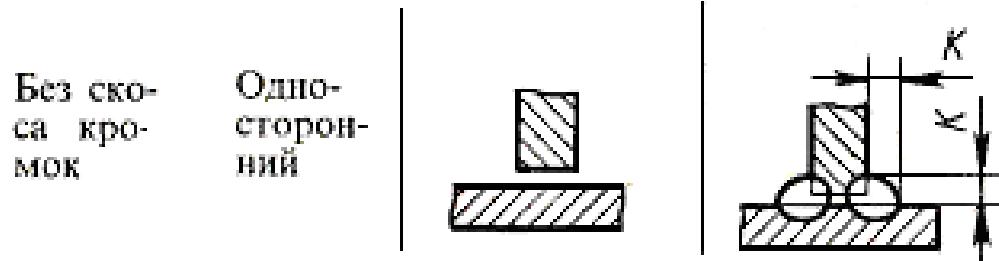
Виды сварных тавровых соединений
